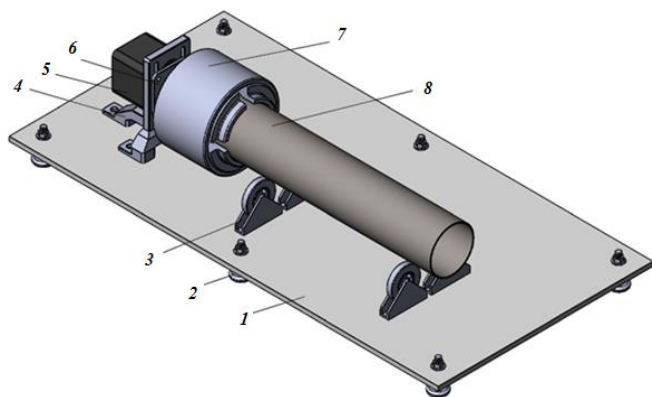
Узел вращения заготовки: 1 – основание; 2 – регулируемые опоры; 3 – роликовые опоры; 4 – держатель для привода; 5 – привод; 6 – узел подшипниковый; 7 – цанговый зажим; 8 – заготовка
